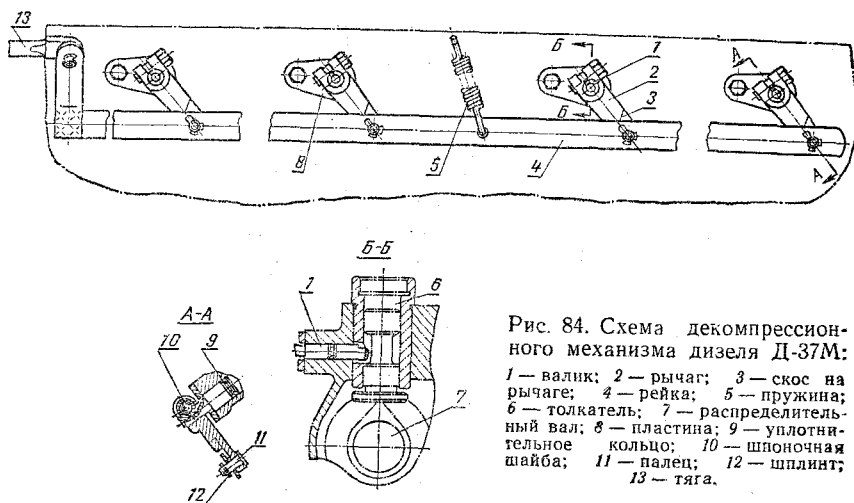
Схема декомпрессионного механизма дизеля Д-37М:
